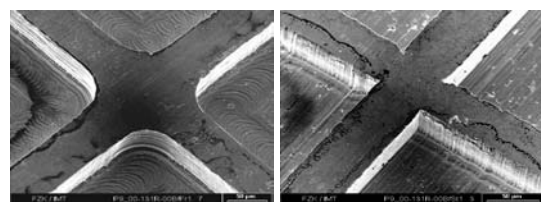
Gefräste Stegkreuzungen mit runden (links) und gehobelte Stegkreuzungen mit scharfen Innenecken (rechts)
